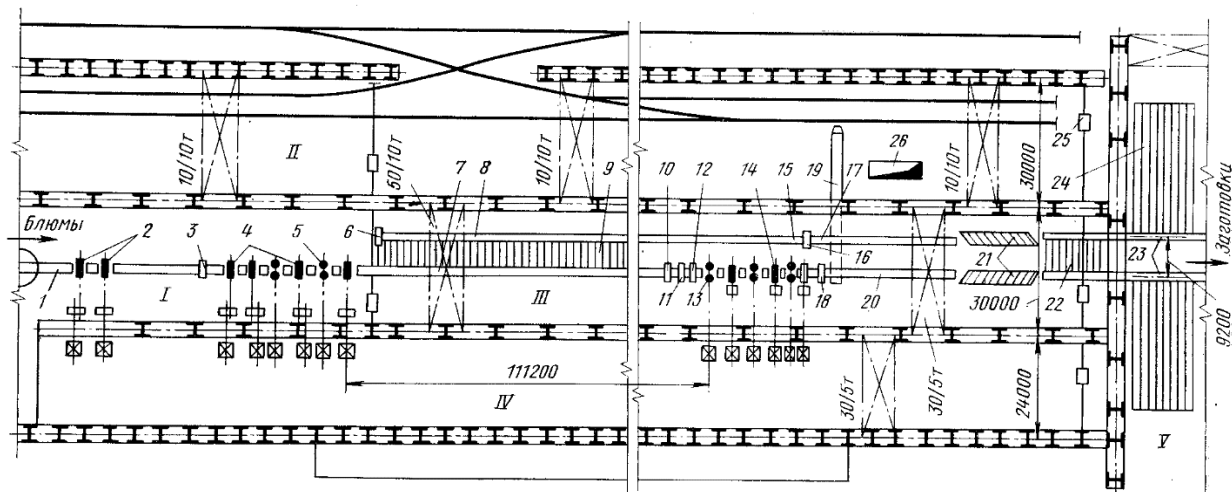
Схема розташування обладнання безперервного заготівельного стану 900/700/500
